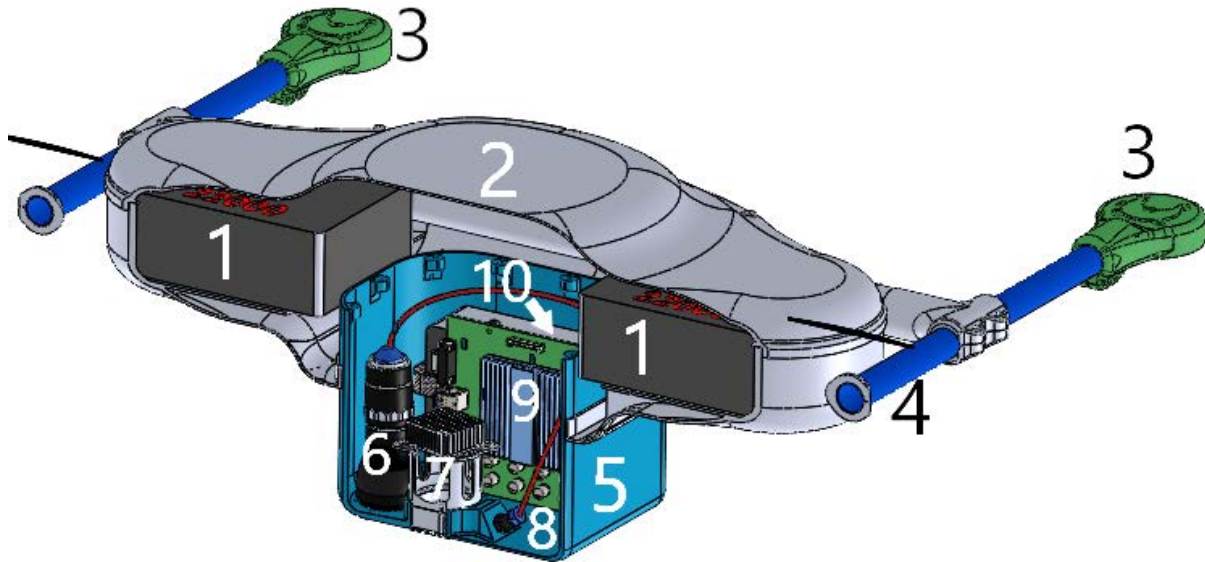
Макет активного спектрометра, вмонтированного в герметичный корпус БВС (вид в разрезе): 1 — аккумулятор 22А/ч, 22В; 2 — герметичный корпус БВС; 3 — крепление силовой установки БВС; 4 — алюминиевая трубка рамы БВС; 5 — герметичный корпус активного спектрометра; 6 — объектив 84UV; 7 — источник света 278нм, 100мВт; 8 — объектив 74-ud; 9 — процессорная плата ITX -N29; 10 — спектрометр Ocean Optics MAYA
